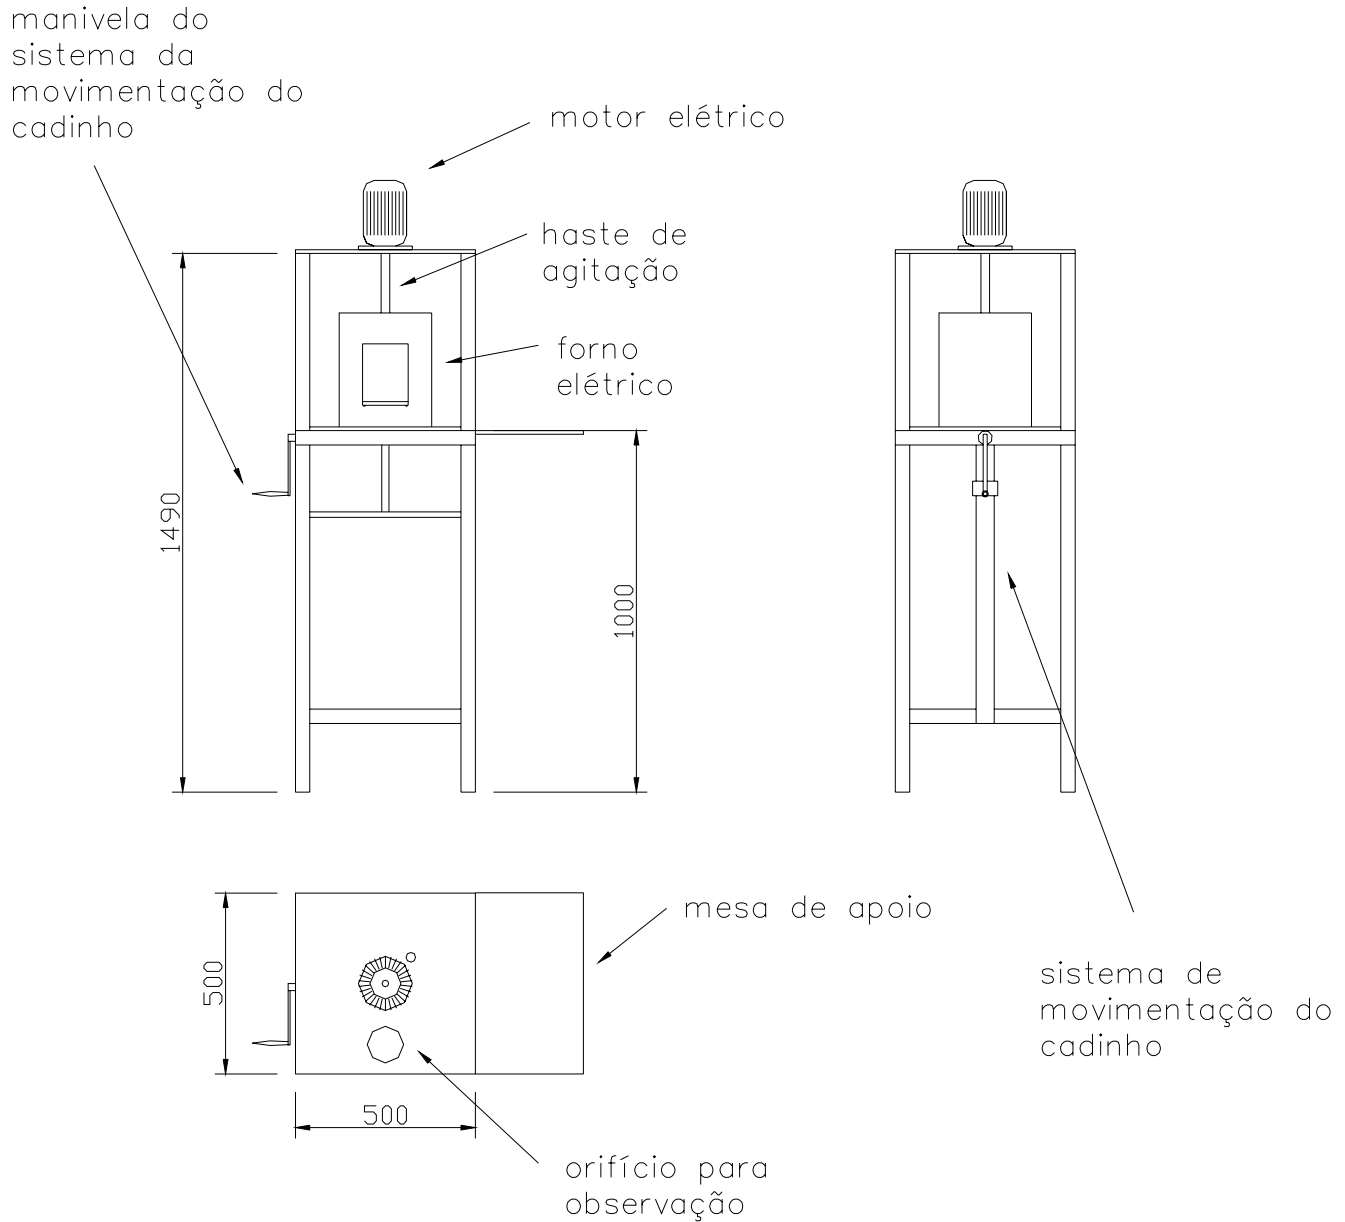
Montagem completa do dispositivo (dimensões em milímetros)
